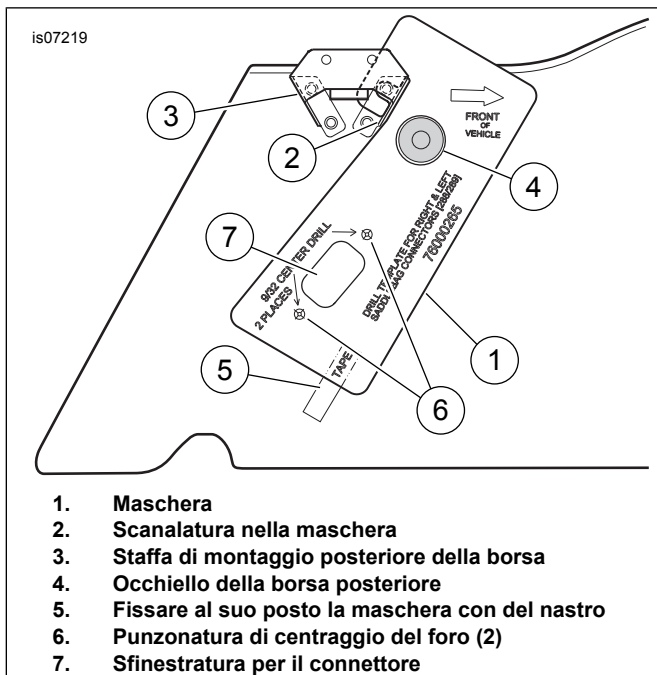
Foratura della borsa per il connettore di montaggio a pannello a 12 vie
